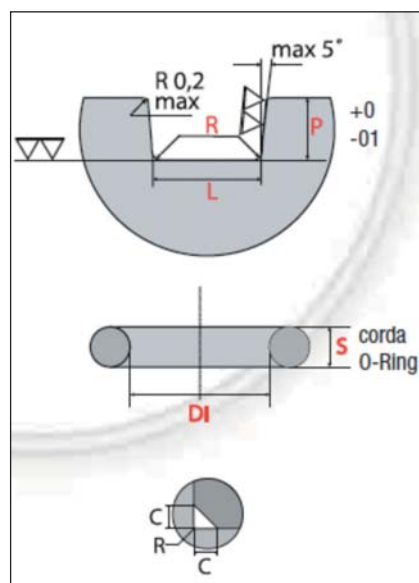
Cava per O-Ring e O-Ring sezionato
